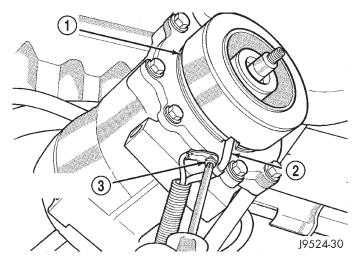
MAZO DE CABLES DE BOBINA DEL EMBRAGUE
